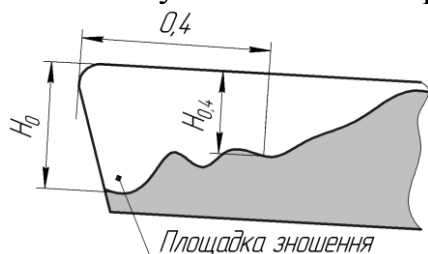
Схема вимірювання зношення на задній поверхні фрези
